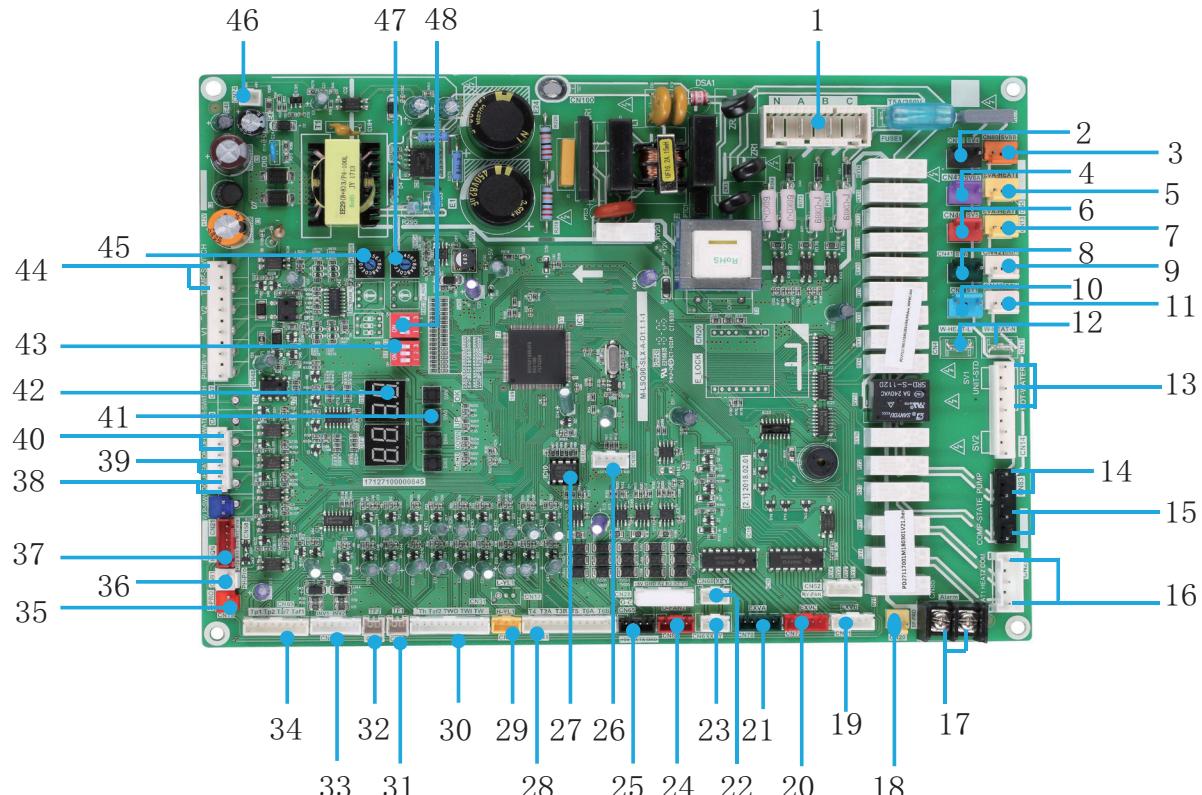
PCB principale dell'unità KEM-90 DNS3
